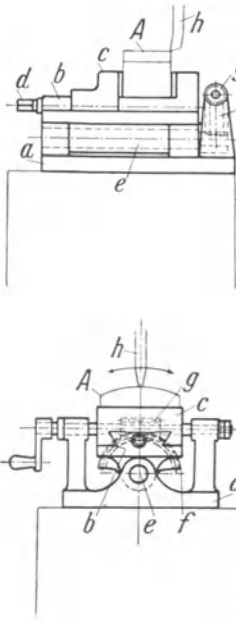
Spannvorrichtung zum Hobeln balliger Flächen.
